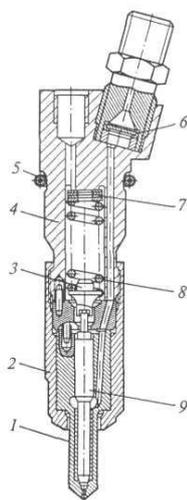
Форсунка: 1 - распылитель; 2 - гайка; 3 - штанга; 4 - корпус; 5 - кольцо; 6 - фильтр; 7 - шайбы; 8 - пружина; 9 – игла.
